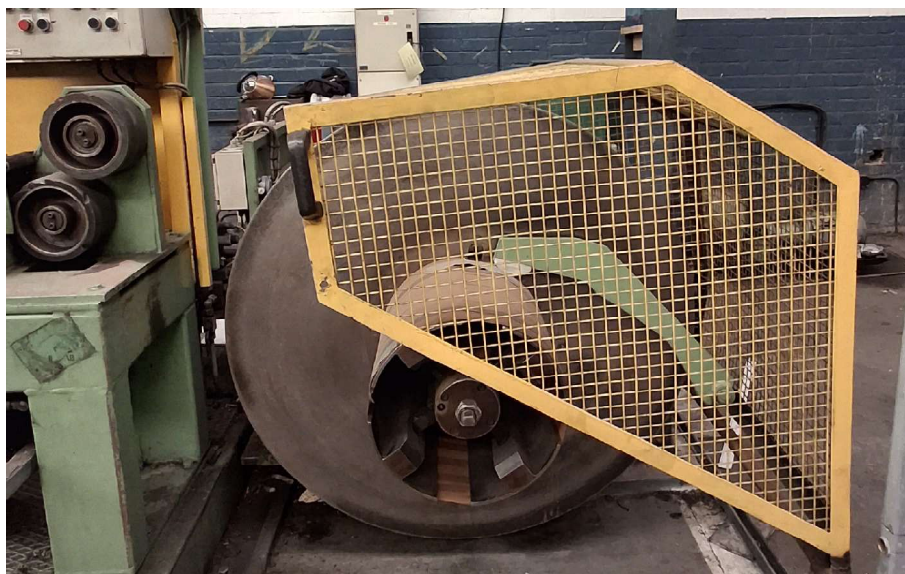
Vista frontal do desbobinador para rolos de até 1t.
